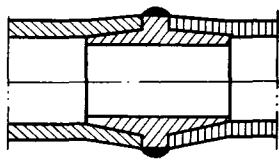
Сварочные кольца для крепления труб внутри бетонного слоя
